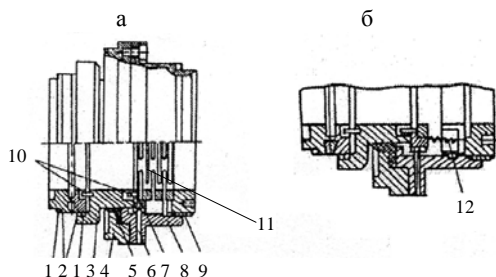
Унифицированный узел торцового уплотнения типа УНИ-2 (а) и фрагмент узла (б) с блоком опорных пружин: 1 – резиновое уплотнительное кольцо; 2 – контактные кольца; 3 – аксиально-подвижная втулка; 4 – фланец; 5 – манжета; 6 – штифт; 7 – обойма; 8 – корпус; 9 – гайка; 10 – штифт; 11 – прорезная пружина; 12 – блок пружин
